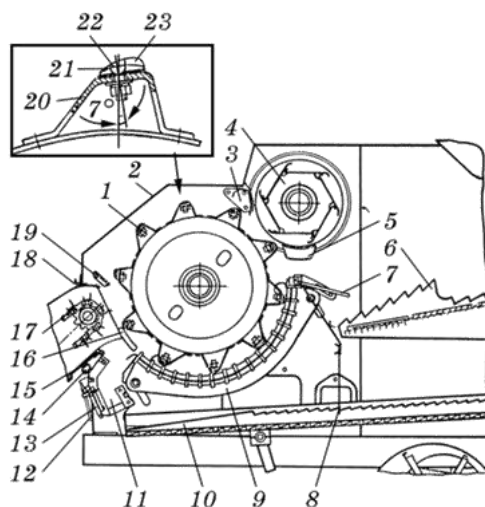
Молотильний апарат комбайна КЗС-9-1: 1 - барабан; 2 - кришка; 3 - відсікач повітряного потоку; 4 - відбійний бітер; 5, 16 і 19 - щитки; 6 - соломотряс; 7 - пальцева решітка; 8 - полотняний фартух; 9 - підбарабання; 10 - струшувати дошка очищення; 11 - камера камнеуловителя; 12 - рукоятка; 13 - відкидна кришка; 14 - труба з роликками; 15 - перехідний щиток; 17 - плаваючий транспортер; 18 - прогумований ремінь; 20 - Планка-подбiчник; 21 - регулювальна пластина; 22 - болт; 23 – бичі.
